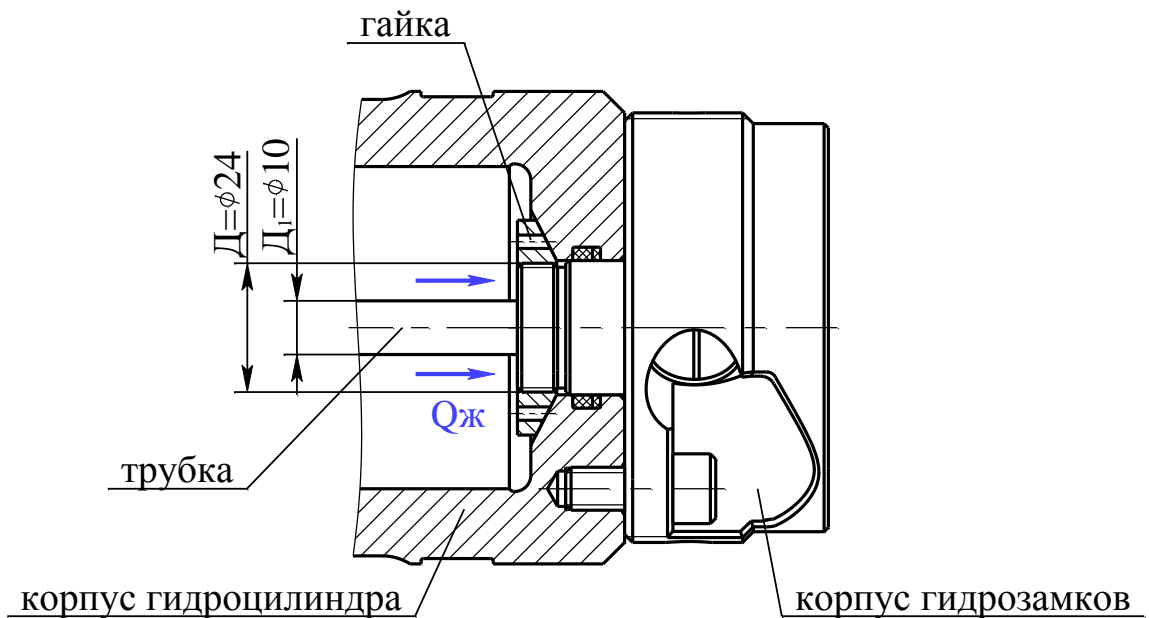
Эскиз для расчета корпуса гидрозамка
